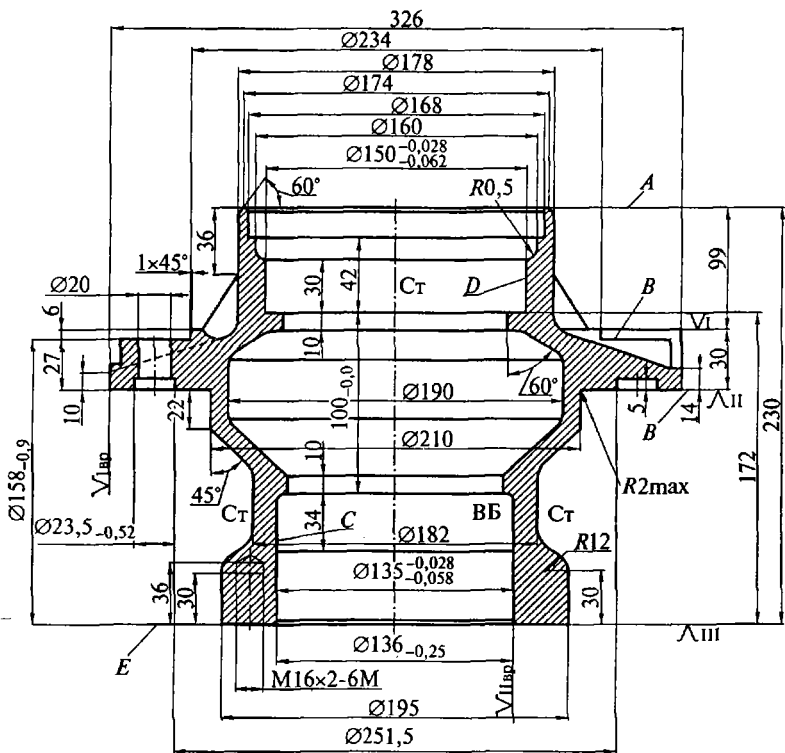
Выбор баз механической обработки на чертеже детали:
